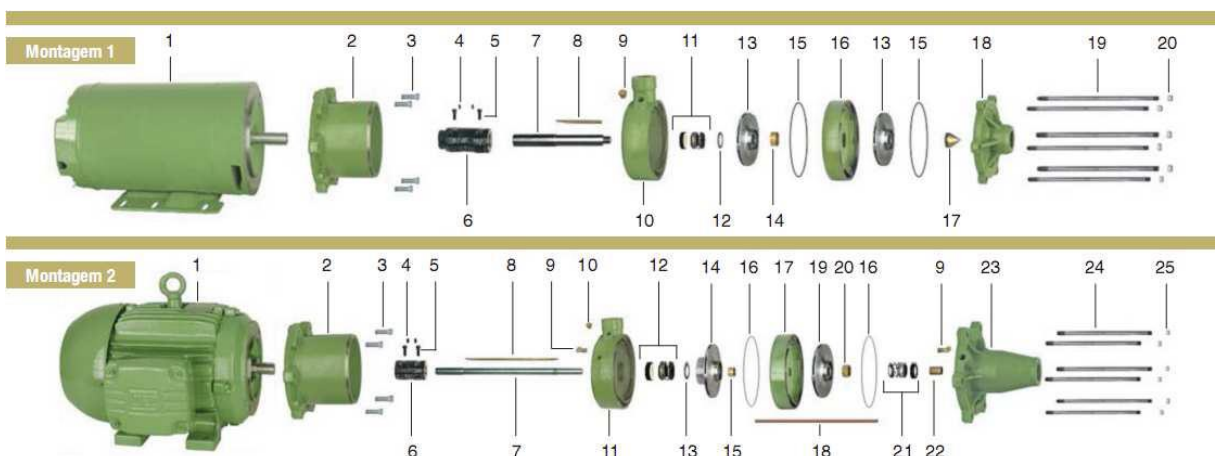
Vista explodida da bomba de simples estágio com seus respectivos componentes
